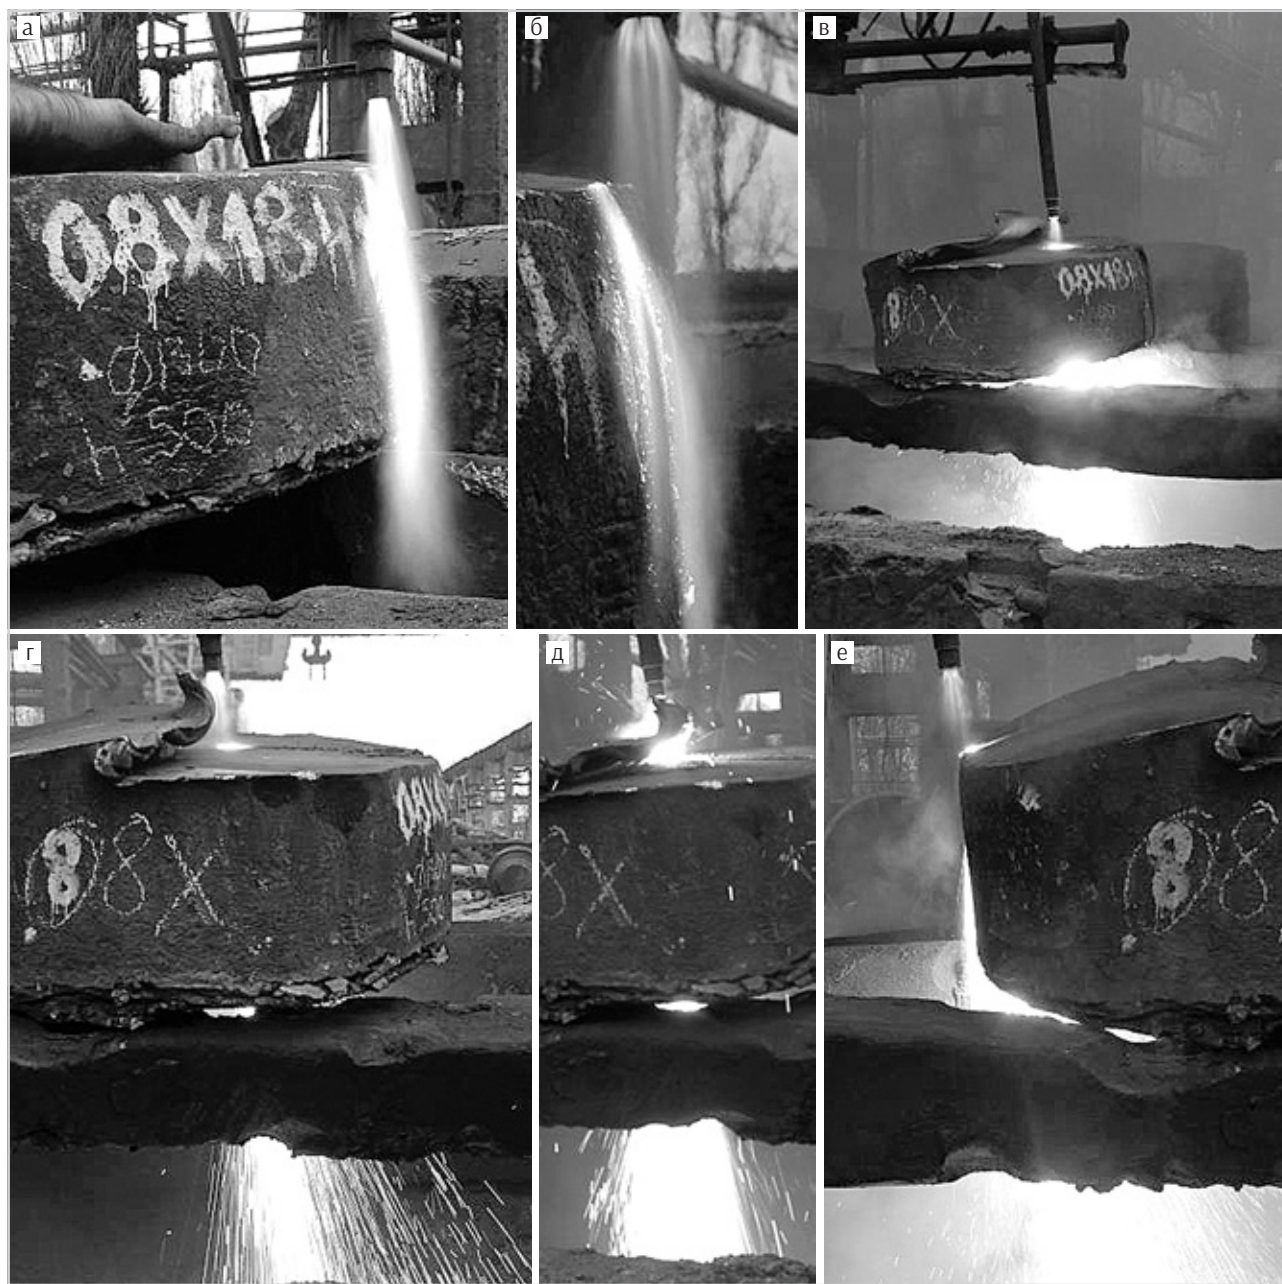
Процесс резки прибыльной части слитка из стали 08X18H10T. Диаметр заготовки 1300 мм, высота 500–600 мм: а — прогрев нижней части заготовки; б — момент пуска основной режущей струи, врезание; в — резка заготовки в ее центральной части; г — резка над заусеницей; д — резка через заусеницу высотой 150 мм; е — выход кислородной струи из заготовки, окончание резки
